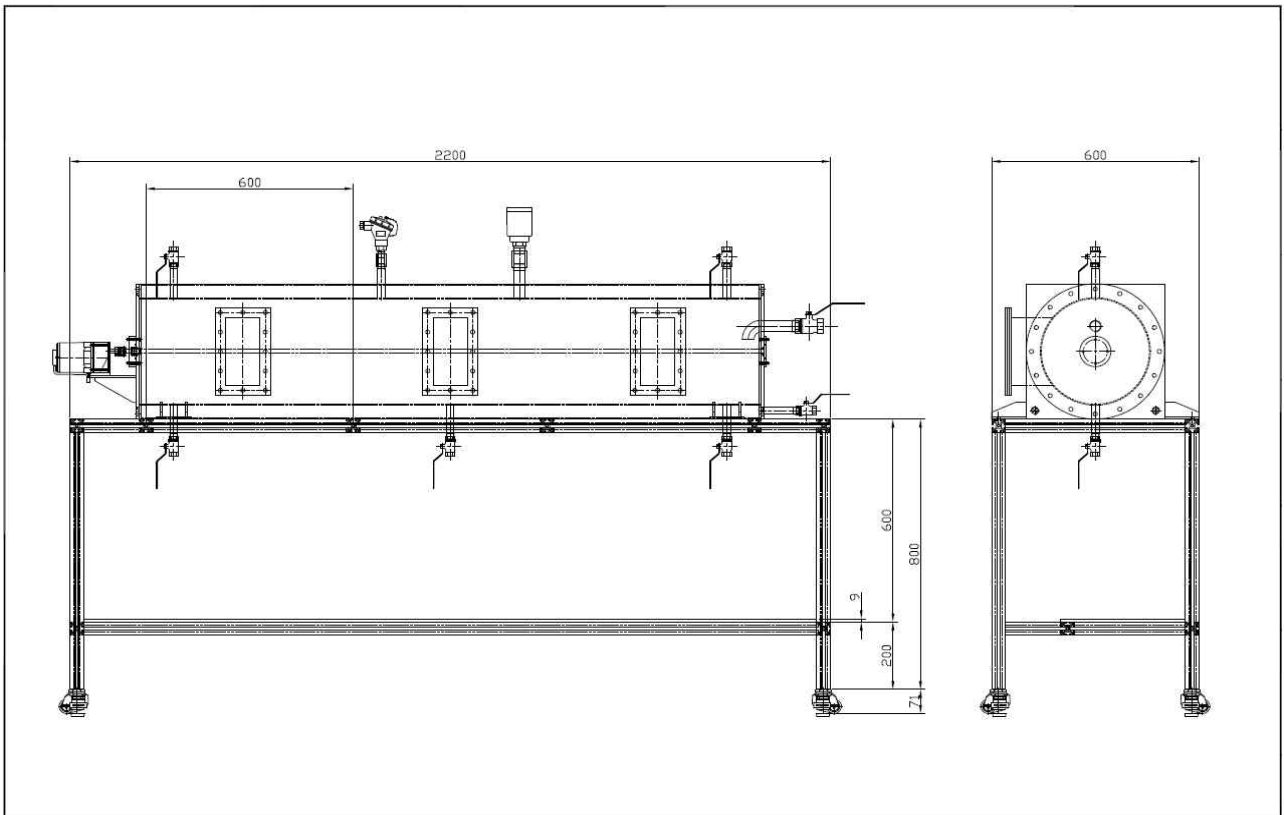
Lab 규모 습식혐기소화 반응기 평면도
